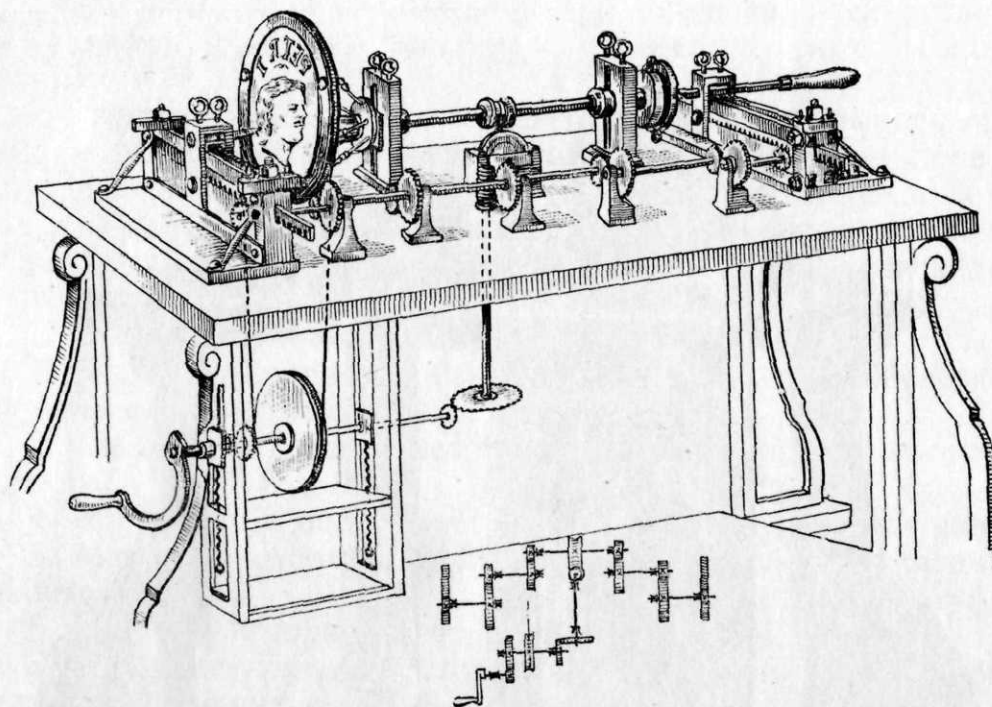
Токарно-копировальный медальерный станок Нартова 1721 г.
